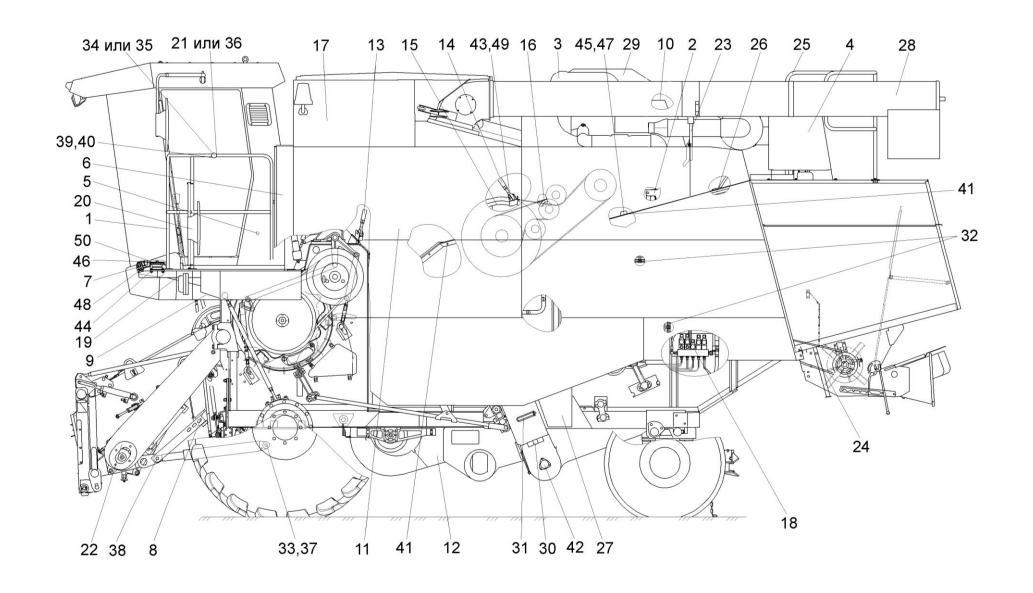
Молотилка самоходная КЗК-10-0100000Б-03 (вид слева)
